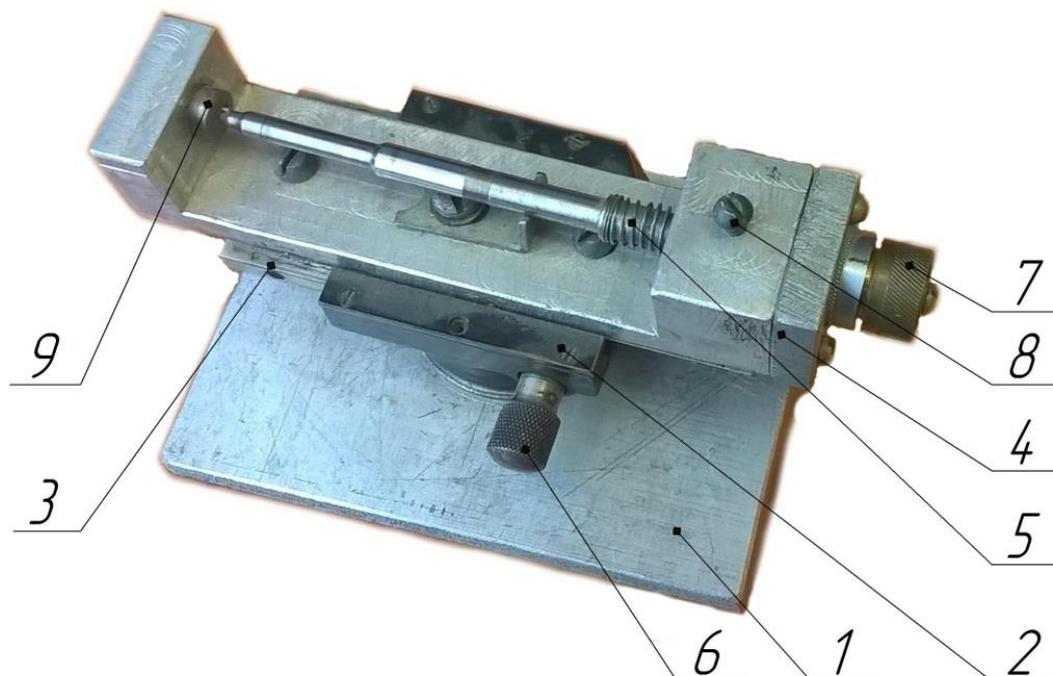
Схема приспособления для нанесения отпечатков на иглах распылителей
